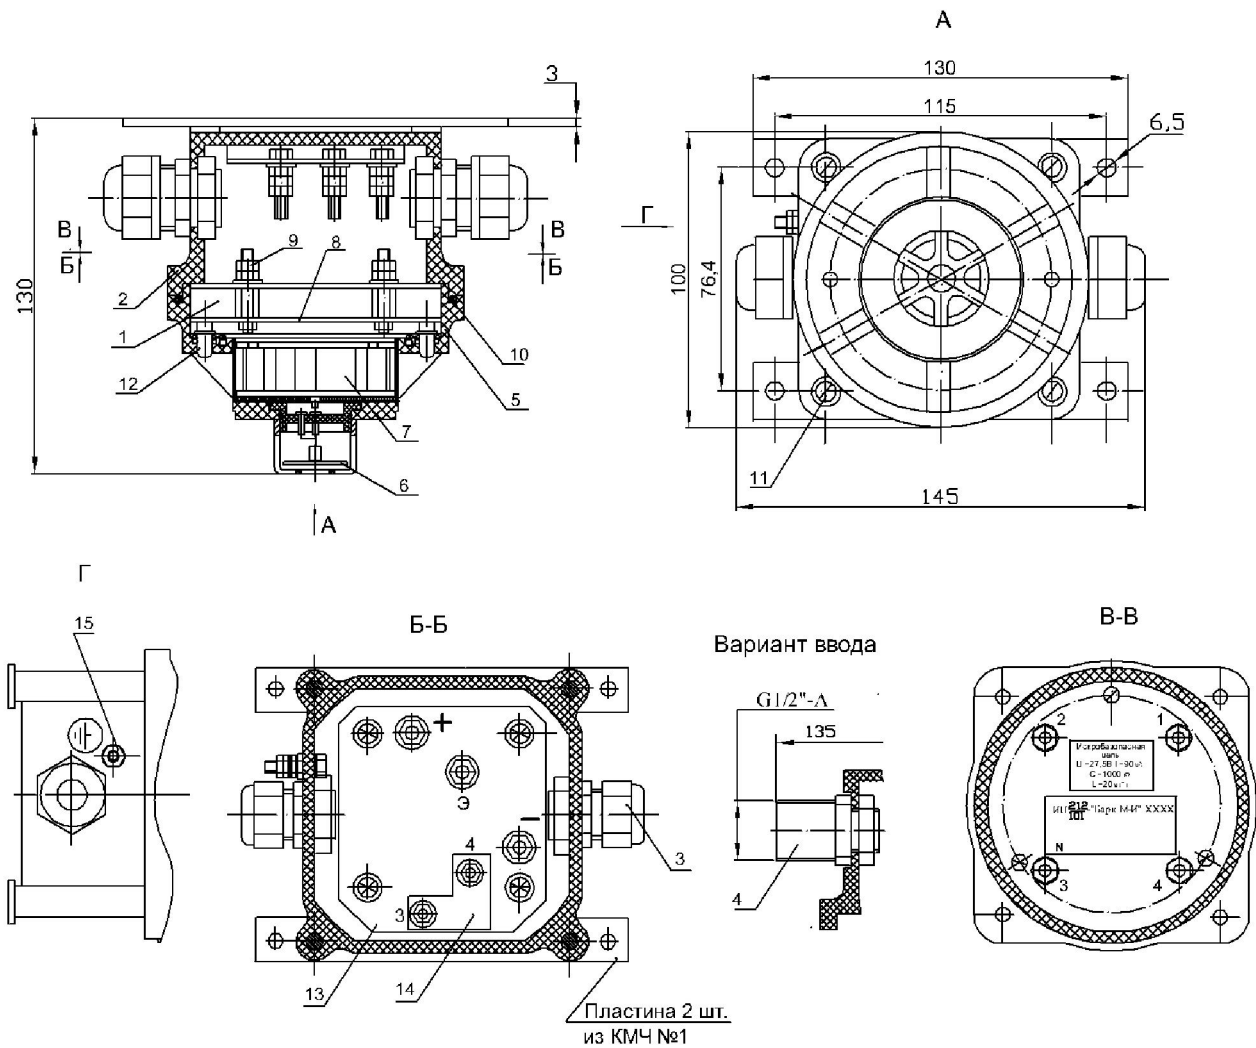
Извещатель пожарный комбинированный искробезопасный ИП212/101 – "Барк М-И" Общий вид. Габаритные и установочные размеры. Крепление извещателя пластинами.
